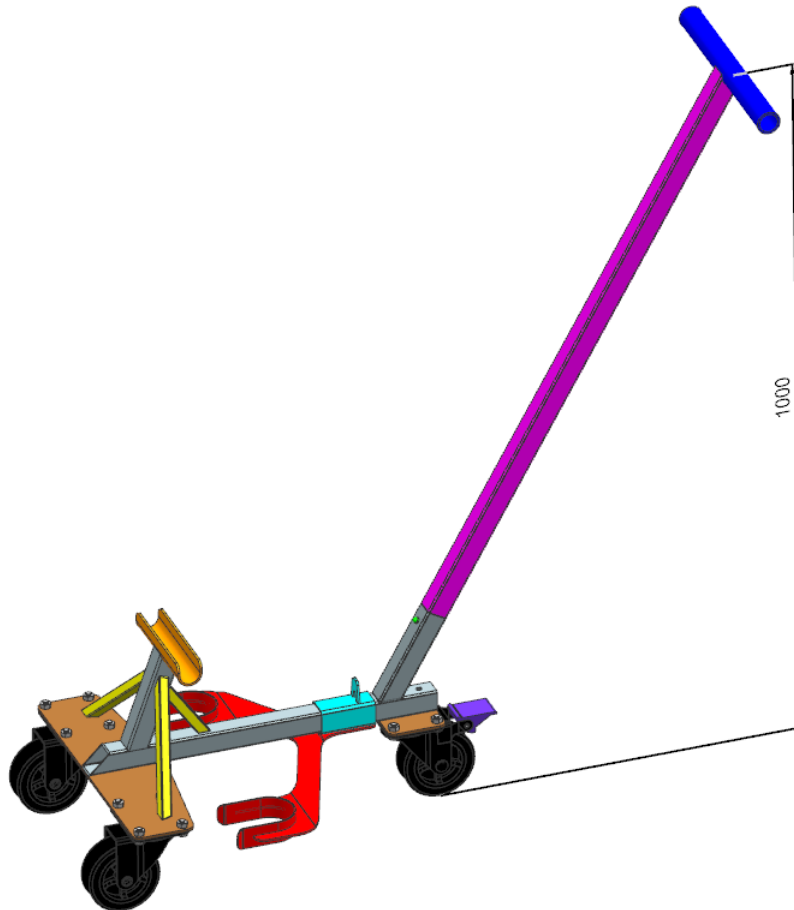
Návrh 8 quick jacku manipulačního se základními rozměry
